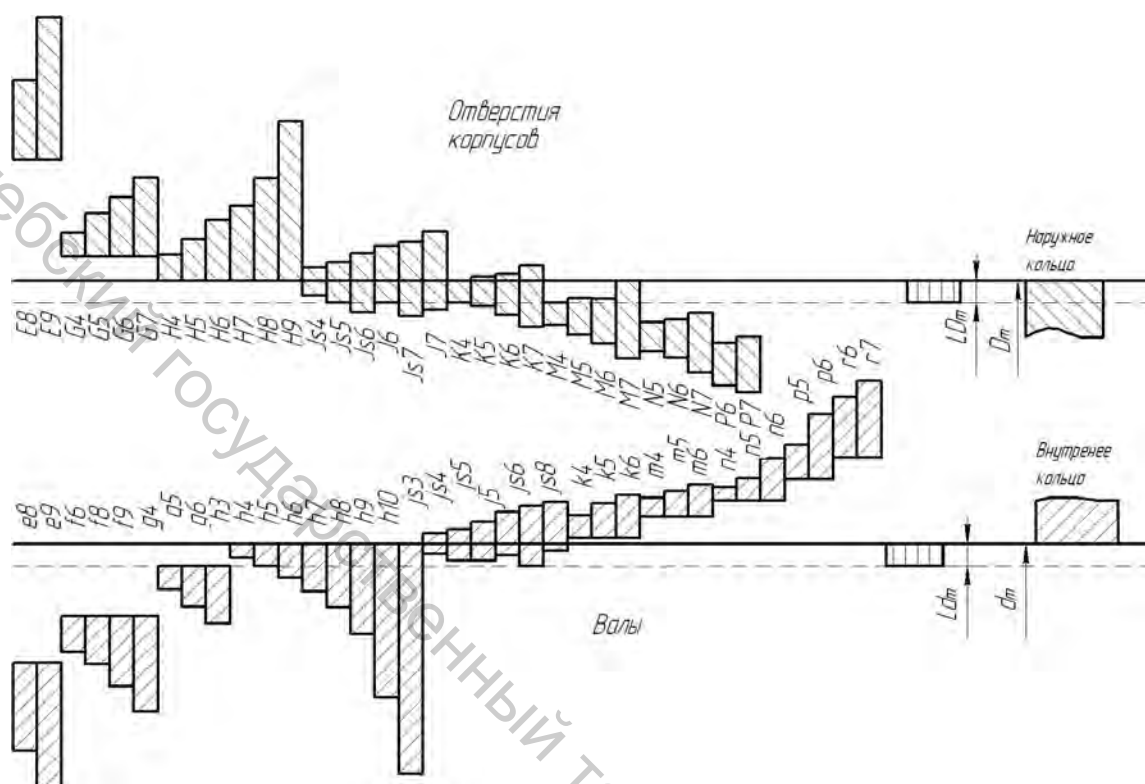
Схема расположения интервалов допусков при посадках подшипников на валы и отверстия корпусов
